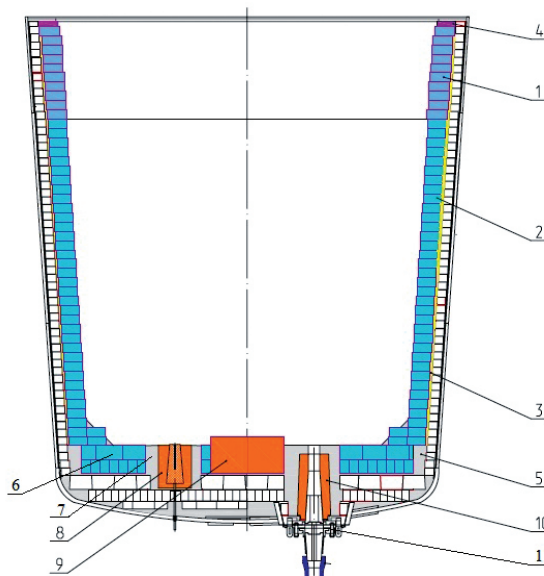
Схема футеровки сталеразливочного ковша:
